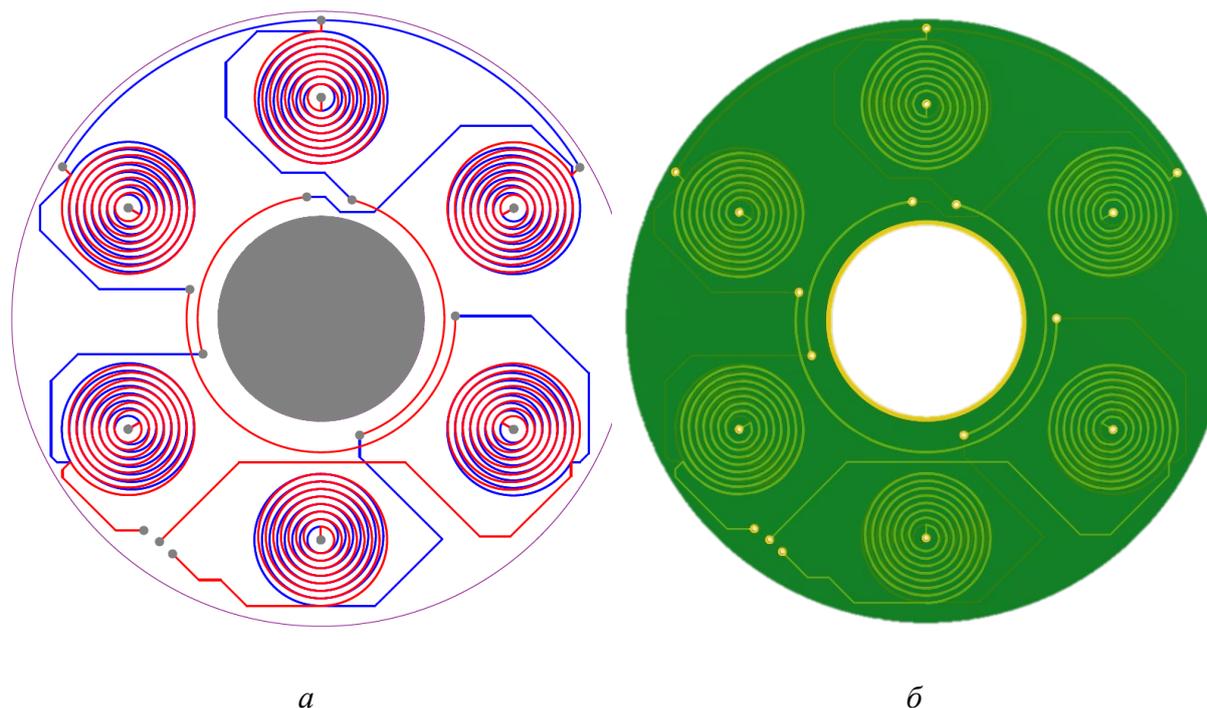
Модель печатного статора с обмотками кругового сосредоточенного типа в Altium Designer: *а* – 2D схема разводки; *б* – 3D прототип
